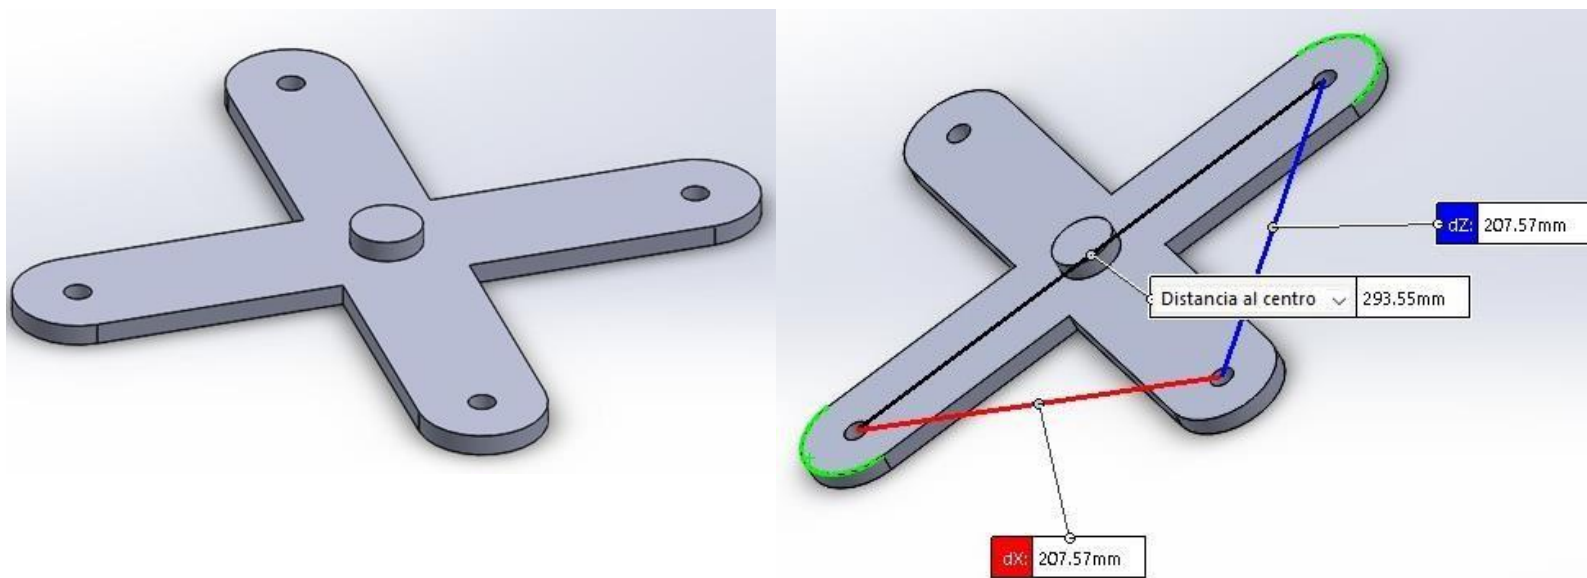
Y 58: diseño y dimensiones de base de pistón.
